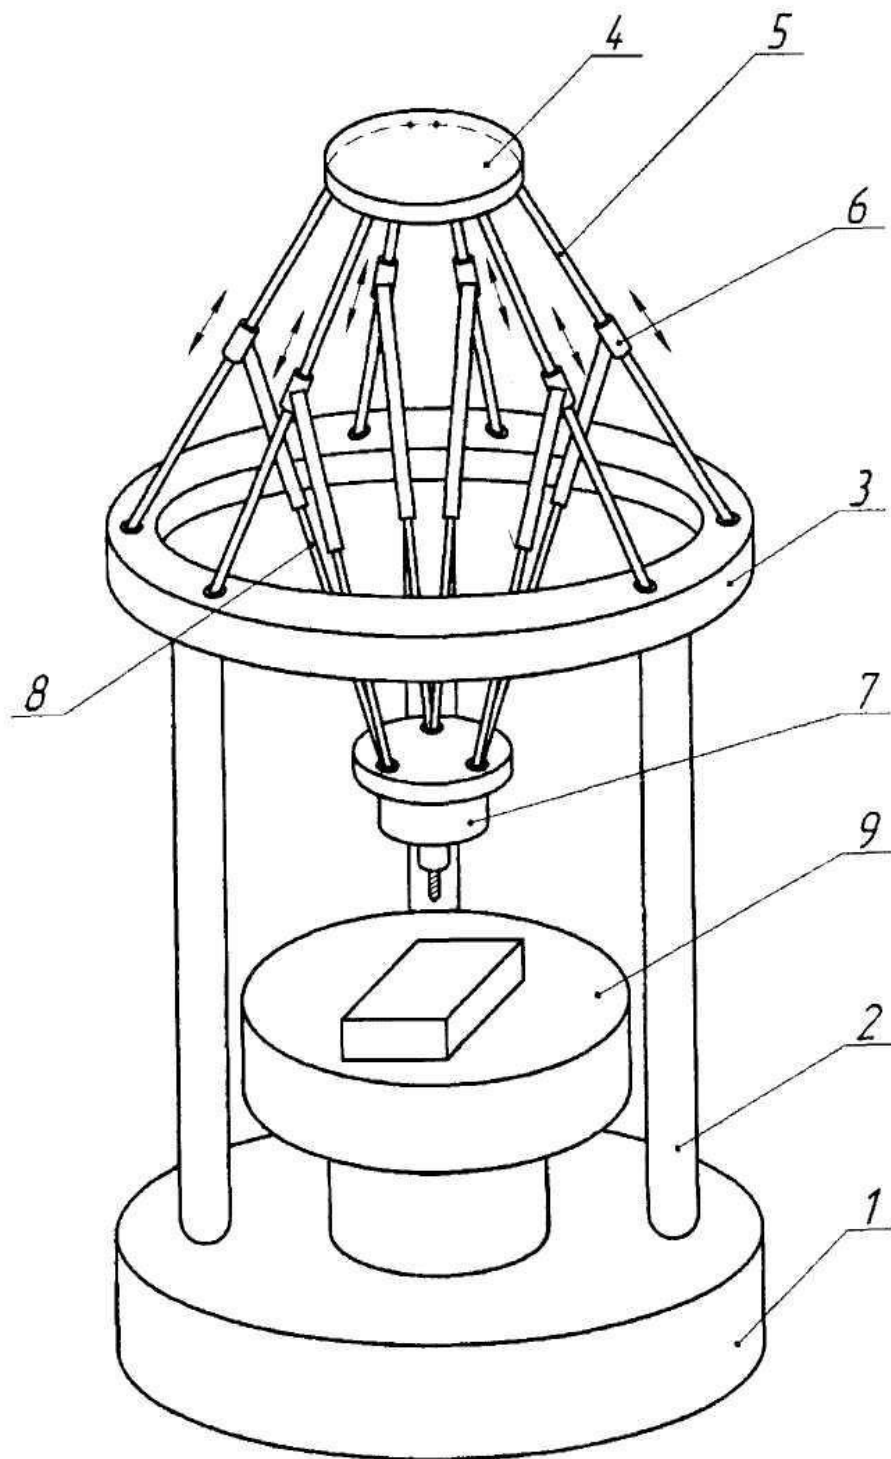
ВЕРСТАТ-ГЕКСАПОД
